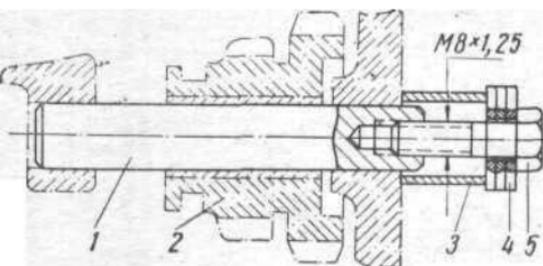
Приспособление для выпрессовывания оси блока шестерен заднего хода
